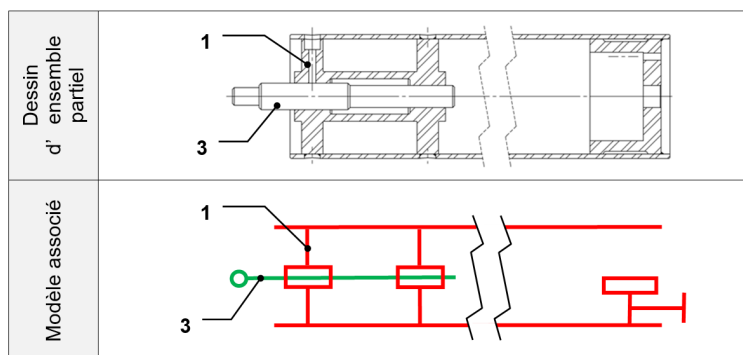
Assemblage rouleau - arbre fou (Dessin d'ensemble partiel - Modèle associé)
